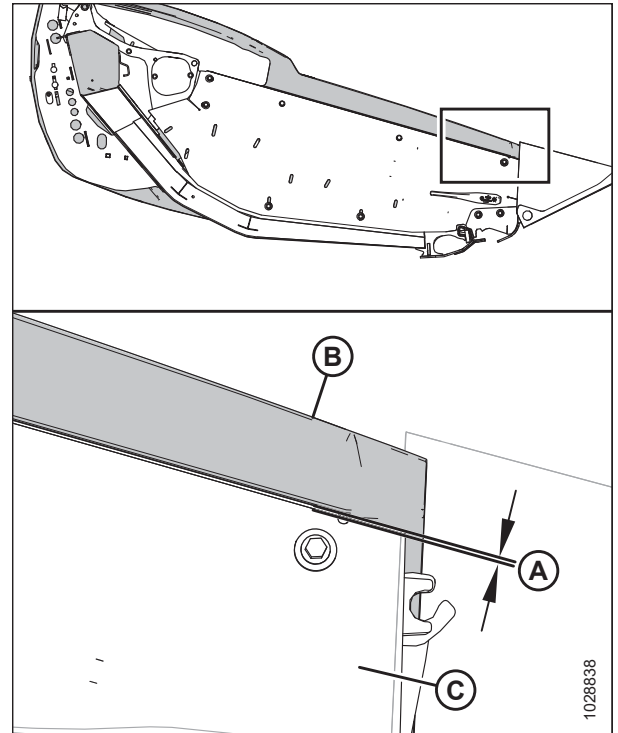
Écart entre le capot de la plateforme et la plaque d'extrémité
